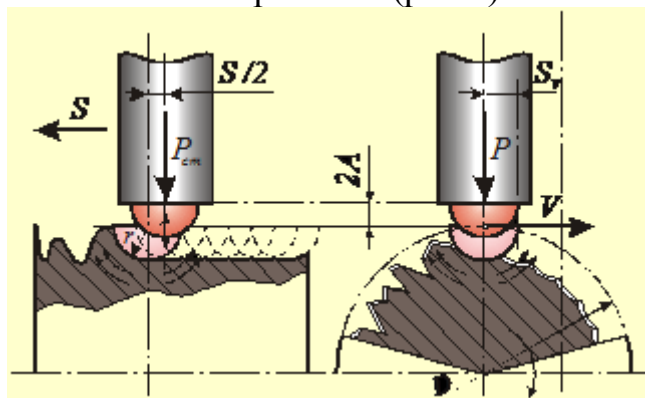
Схема поверхностного пластического деформирования при ультразвуковой упрочняющей обработке
